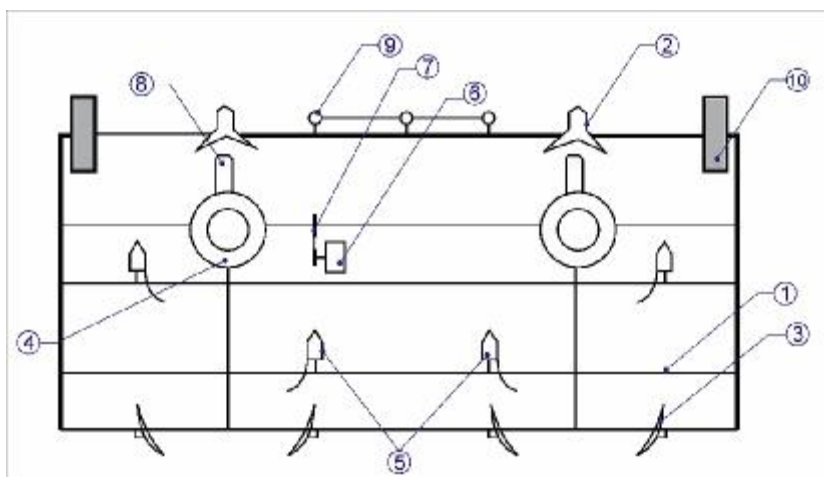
Компоновочная схема размещения рабочих органов агрегата на раме 1-рама;2- рыхлители;3- сферические диски, 4- бункер для удобрений, 5- право – левообарачивающие корпуса; 6,7-приводной механизм туковысевающего аппарата; 8-сошник для ленточного двухслойного внесения удобрений; 9- навеска;10-опорное колесо.
